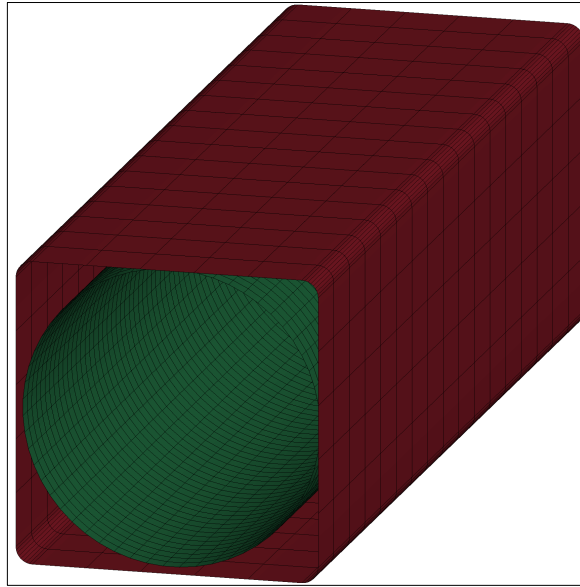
Kenar bükme prosesi geometrik detaylar (Ölçüler mm olarak verilmiştir)
